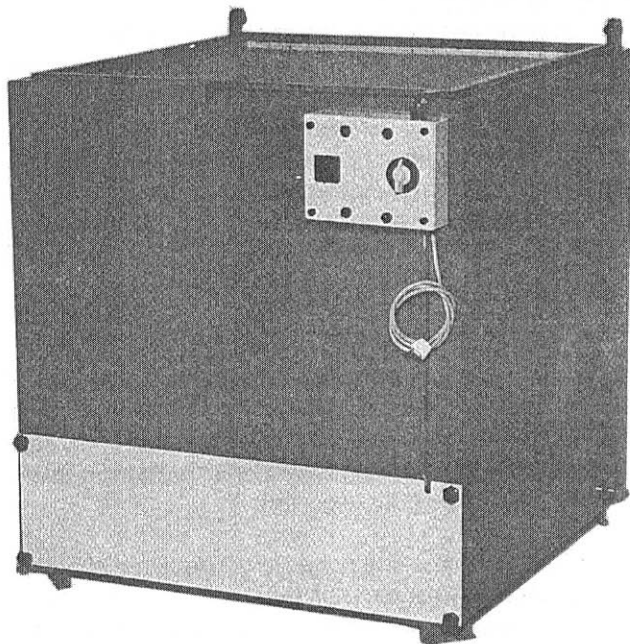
Aspecto exterior que presenta una máquina lavadora y desengrasadora de piezas mecánicas, de funcionamiento rotativo.
